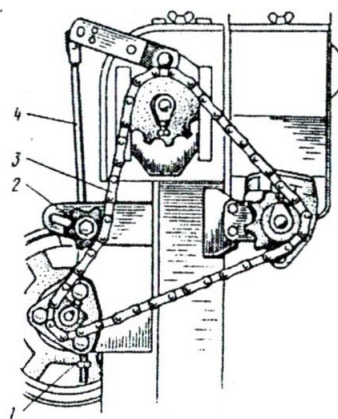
Елеватор зерновий: 1 – гайка; 2 – зірочка натяжна; 3 – штанга
